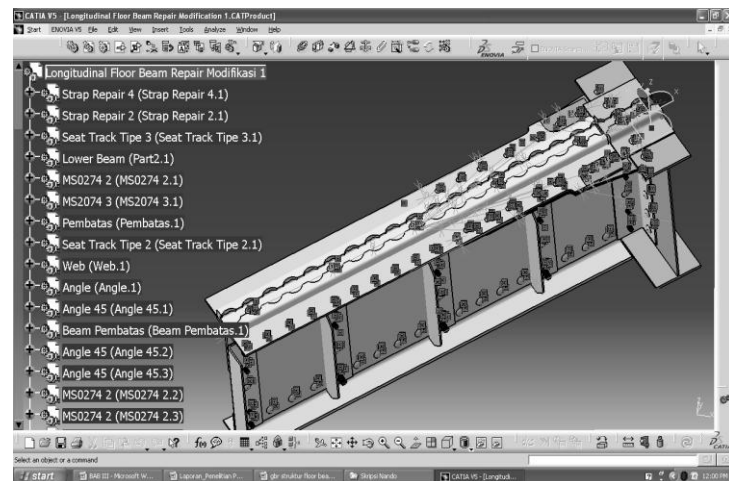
Part* yang menyusun struktur *longitudinal floor beam
